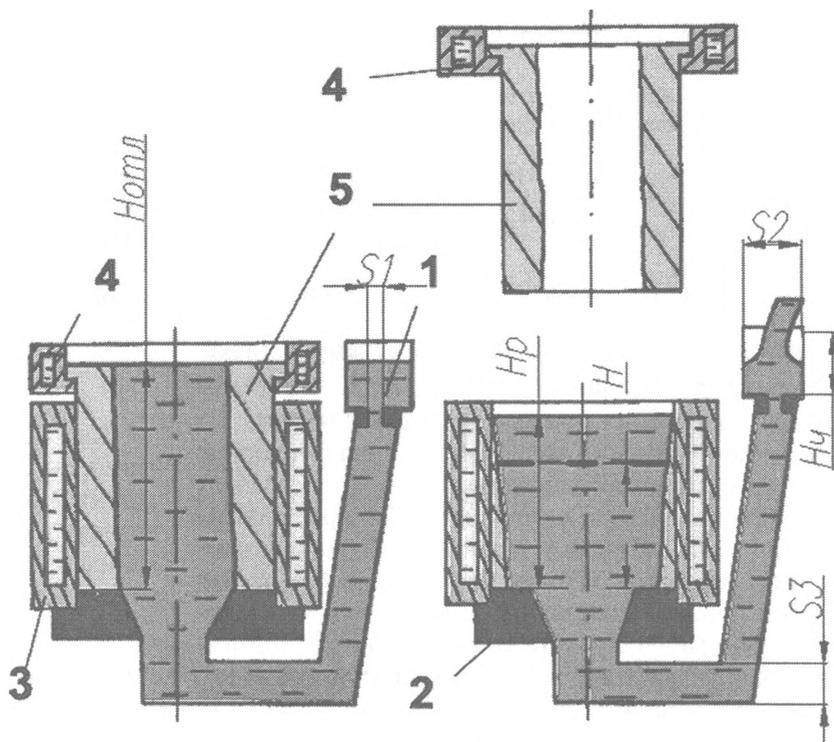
Принципиальная схема непрерывно-циклического литья полых заготовок без стержня: 1 — металлопровод; 2 — соединительный стакан; 3 — стационарная часть кристаллизатора; 4 — подвижная часть кристаллизатора (захваты); 5 — отливка
